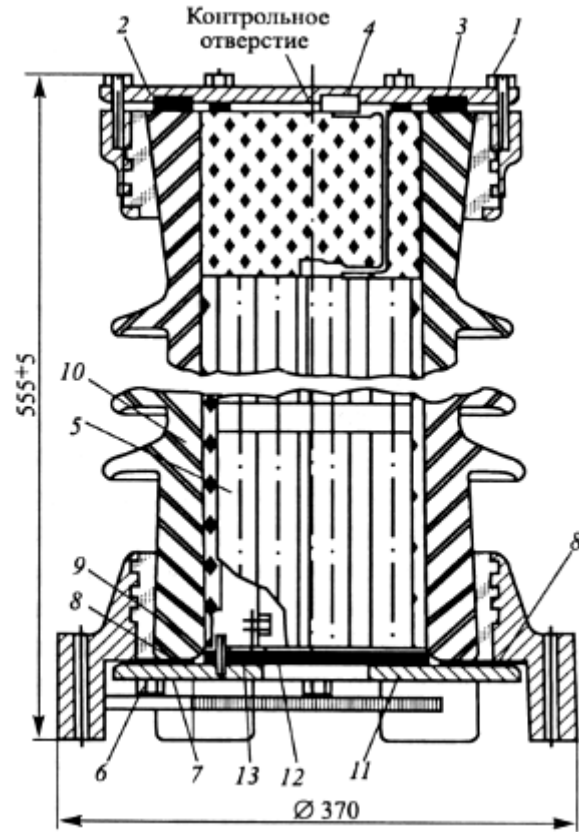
Ограничитель перенапряжений нелинейный ОПН-25: 1, 6, 9 - болты; 2- верхняя крышка; 3, 8, 13 - резиновая уплотнительная прокладка; 4 - гайка; 5 - блок нелинейных резисторов; 7 - днище; 10 - фарфоровый кожух; 11 – кольцо; 12 - мембрана
